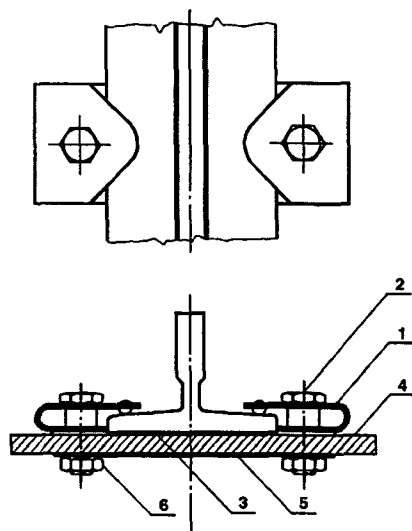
Крепление направляющей с помощью пружинных прижимов (British Guide Rails Ltd)
